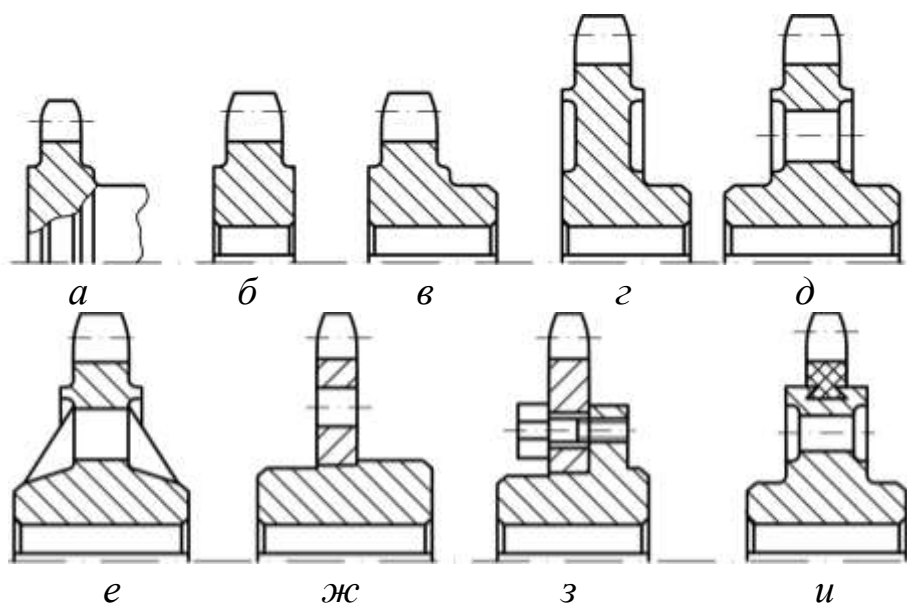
Конструкции звездочек: а – вал-звездочка; б – звездочка без ступицы; в – звездочка со ступицей; г, д – звездочки дисковой конструкции; е – звездочка литая дисковой конструкции с ребрами; ж – звездочка сварная; з – звездочка составная; и – звездочка, венец и ступица которой выполнены из различных материалов
